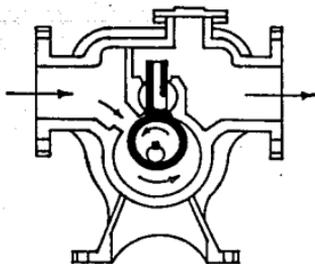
BOMBA ROTATORIA DE LEVA Y PISTON.
